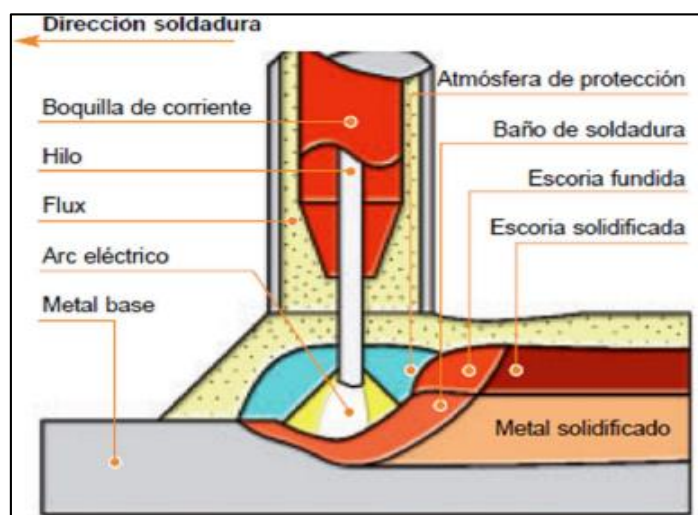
Proceso de soldadura por arco sumergido SAW
